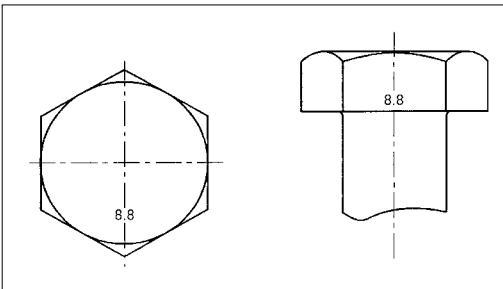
Abb. G: Beispiel für die Kennzeichnung von Sechskantschrauben
